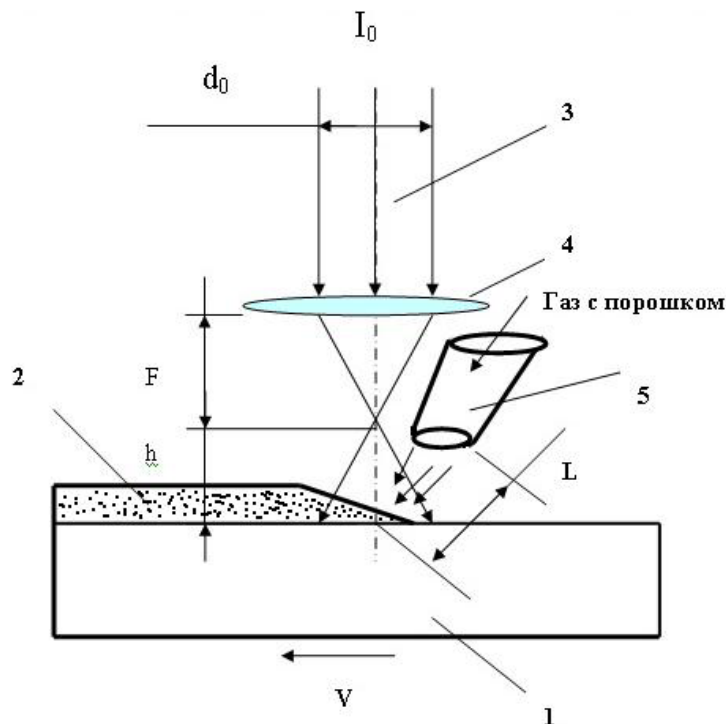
Схема ЛТУ для газопорошковой наплавки:
